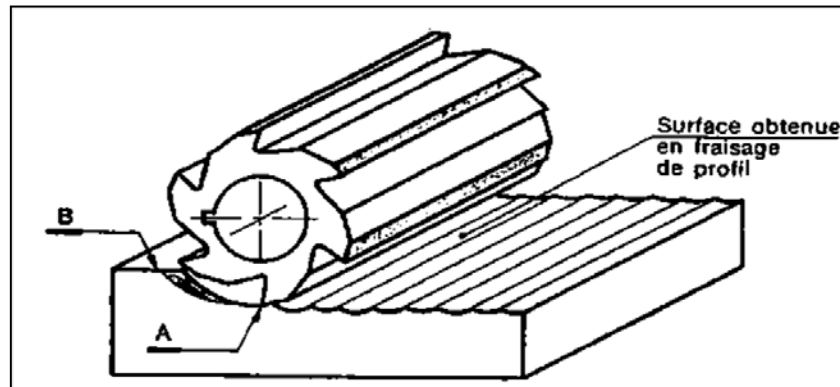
Fraisage de profil A arrête tranchante de la fraise, B la pièce usinée [2].
